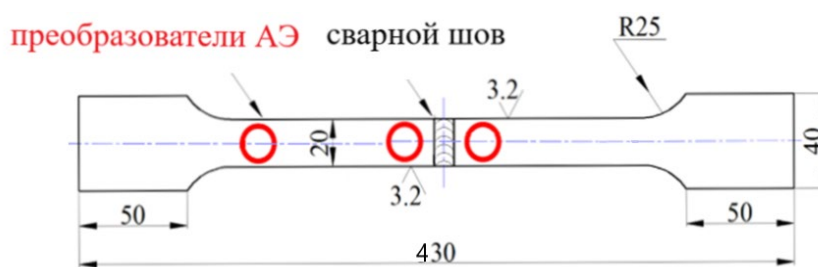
Схема образца разнородного сварного соединения стали 20 и 12Х18Н10Т
